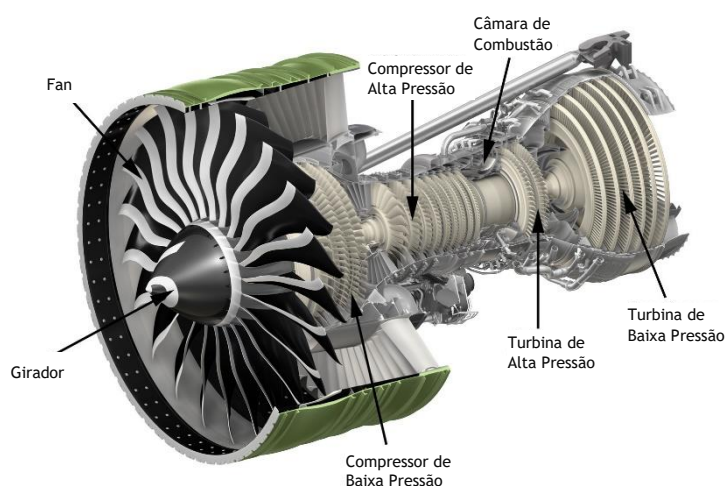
Esquematização dos componentes do motor GE-90 [33].
